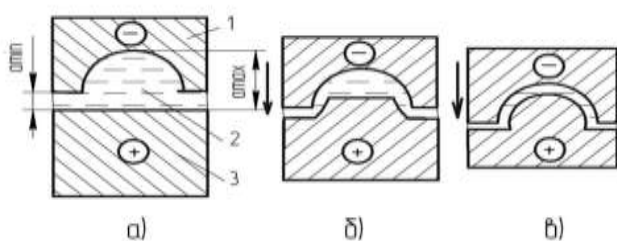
Схема размерной электрохимической обработки с одним перемещающимся электродом-инструментом: 1-электрод инструмент, 2- электролит, 3- заготовка-анод [3].
